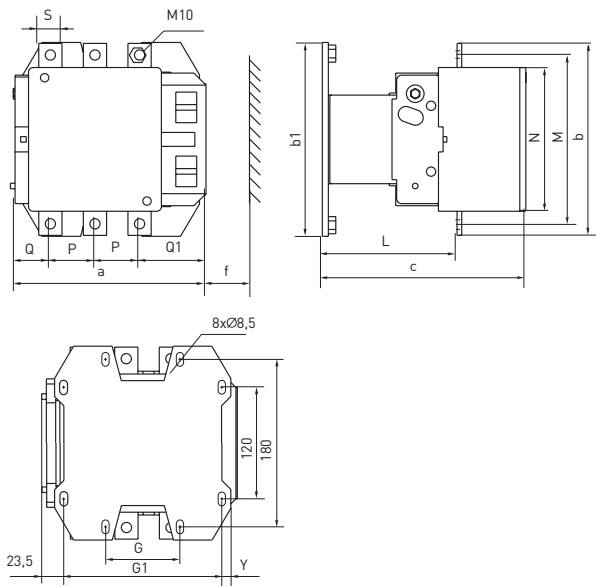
Габаритные и установочные размеры КТЭ-2 (400А; 500А)
